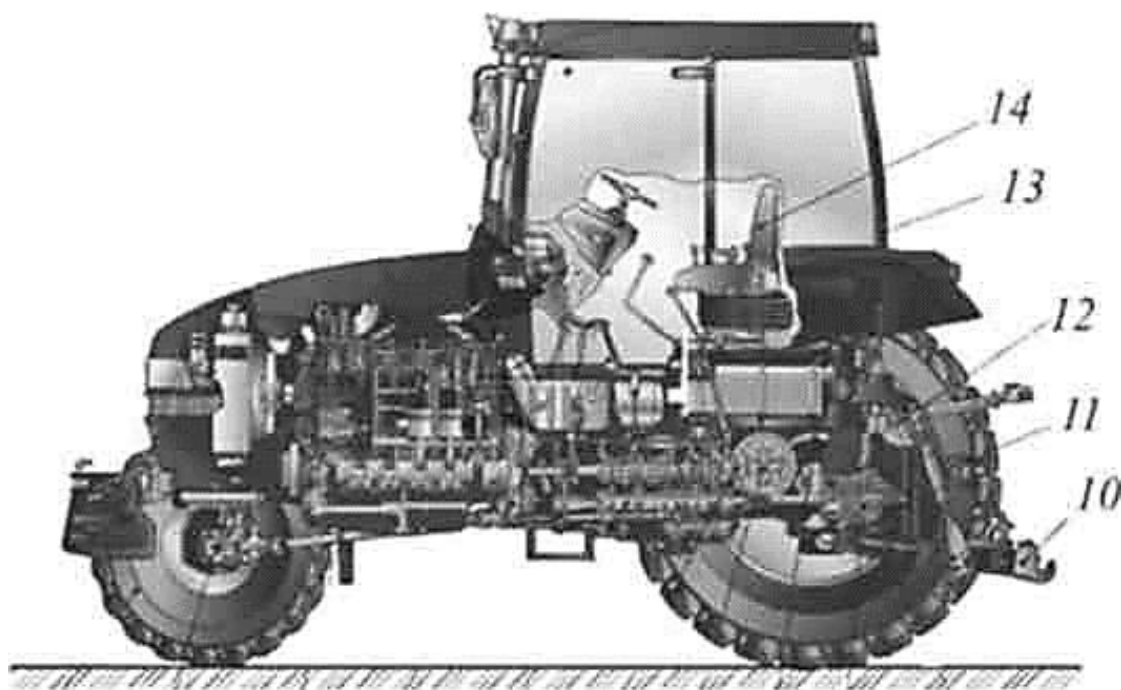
Схема расположения основных агрегатов и узлов колесного трактора
